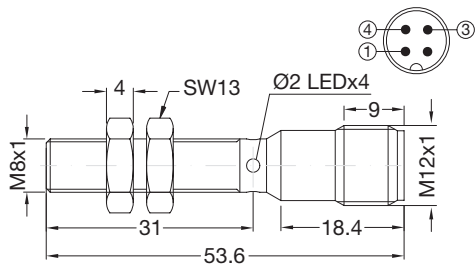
Kurze Ausführung, bündiger Einbau, M12 Steckversion
